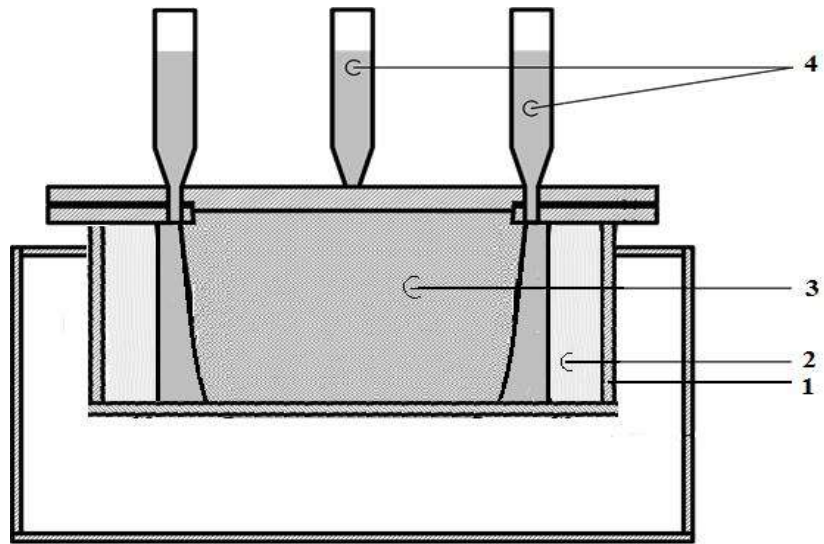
Схема формового комплекта для футеровочного элемента – кольца: 1 - перфорированный металлический каркас; 2 - влагопоглощающая форма; 3 - непористый сердечник; 4 - подпиточные емкости для шликера.
